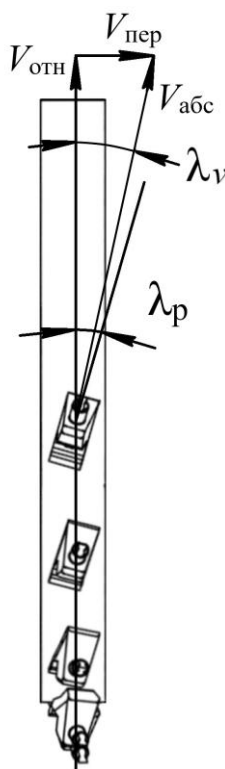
Схема установки резцедержателей на поверхности диска, предусматривающая наличие угла разворота резцов  $\lambda_p$  относительно плоскости диска
